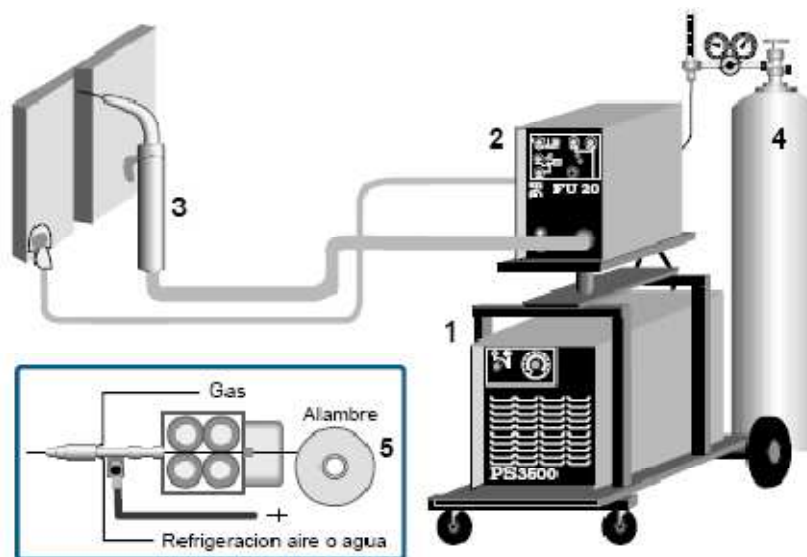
Esquema del equipo de soldadura GMAW
